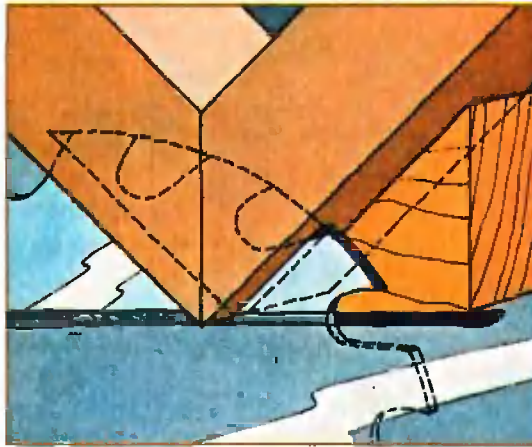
Схема сборки каркаса приставного столика. Вид сверху.
